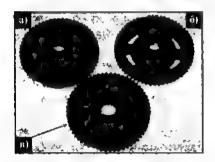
Внешний вил шкива колсивала: а - с резиновым демпфером: б - чугунного: в - с резиновым демпфером, для 16-клапанного двигателя ВАЗ-2112 (с увеличенным посадочным диаметром).
